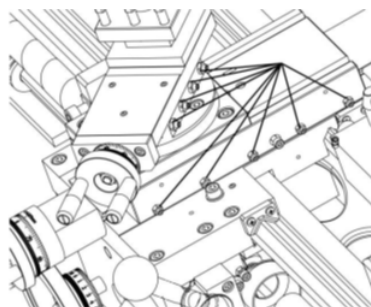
Винты направляющих поперечного и крестового суппортов.
